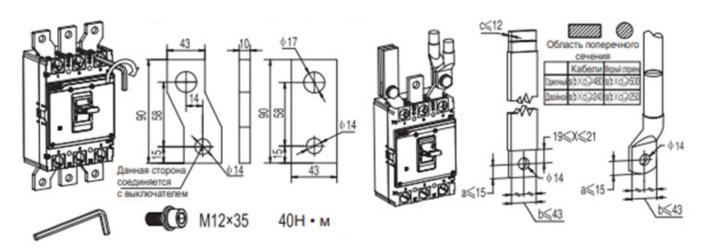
NXM-800 размеры соединительной пластины и кабелей
